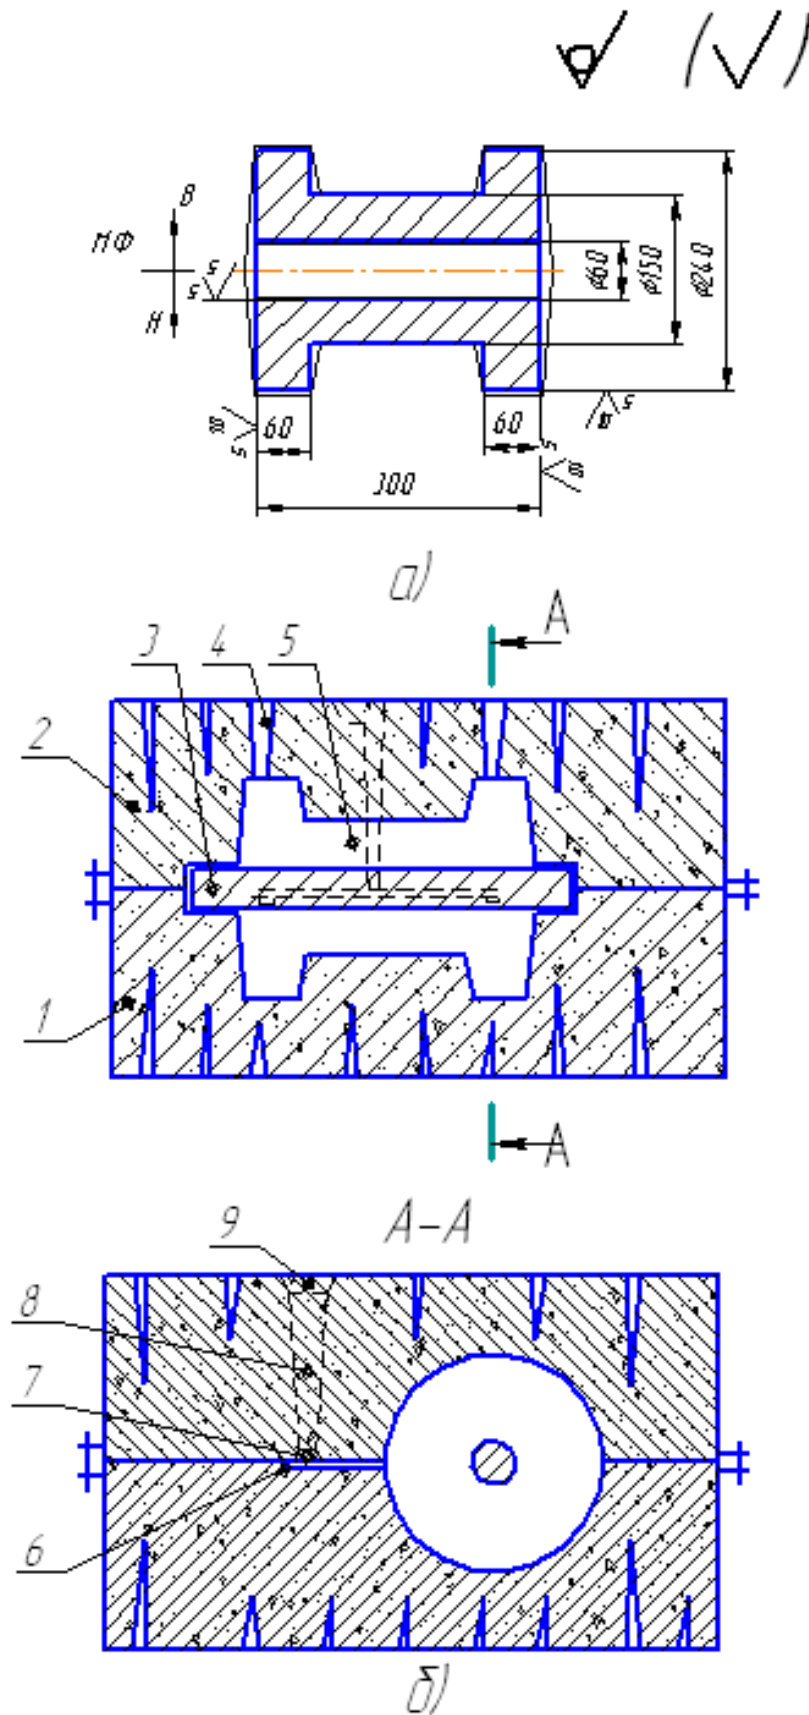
Чертеж отливки и ее расположение в литейной форме
